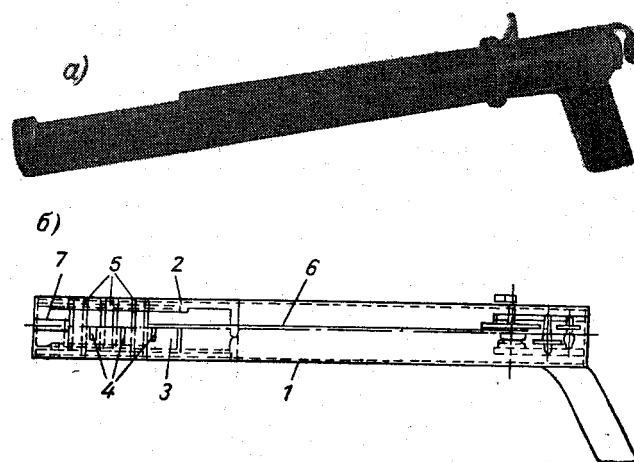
Внешний вид и схематический чертеж заборника капель.
